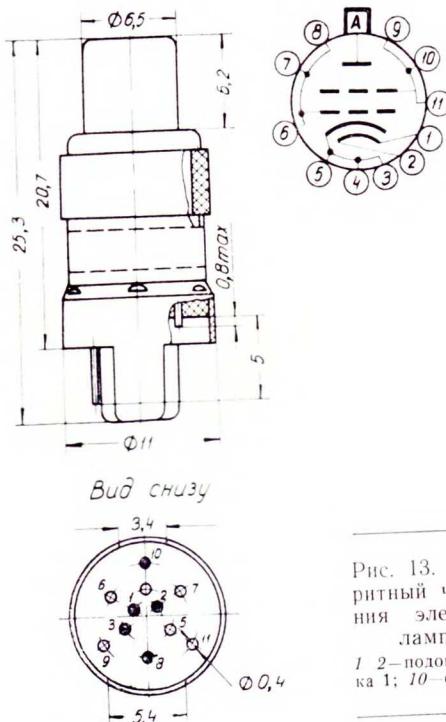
Внешний вид, габаритный чертеж, схема соединения электродов с выводами ламп 6Э13Н и 6Э14Н
